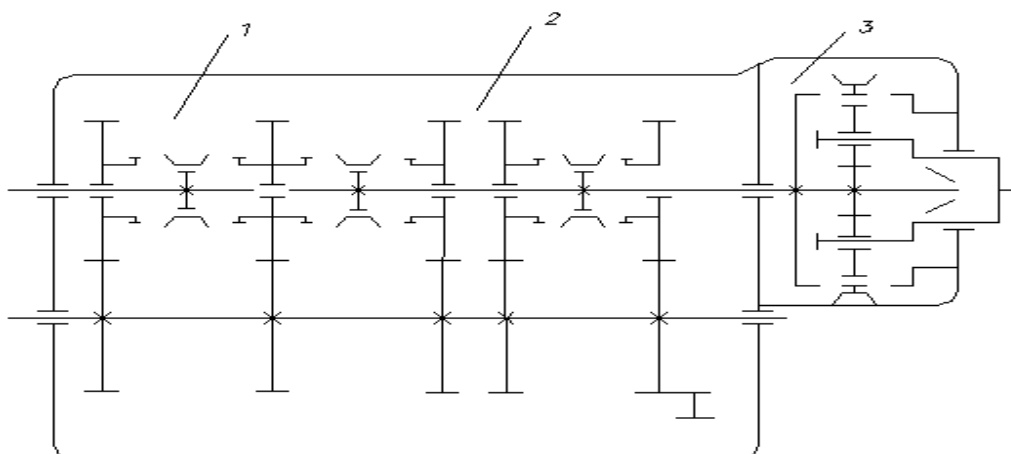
кинематическая схема 12– ступенчатой коробки передач.
